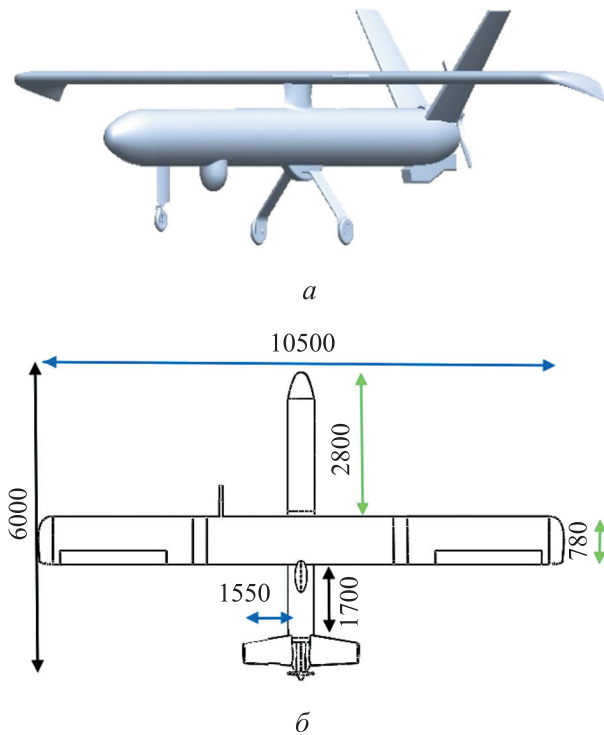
Внешний вид (а) и конструктивная схема (б) БПЛА Hermes 450
